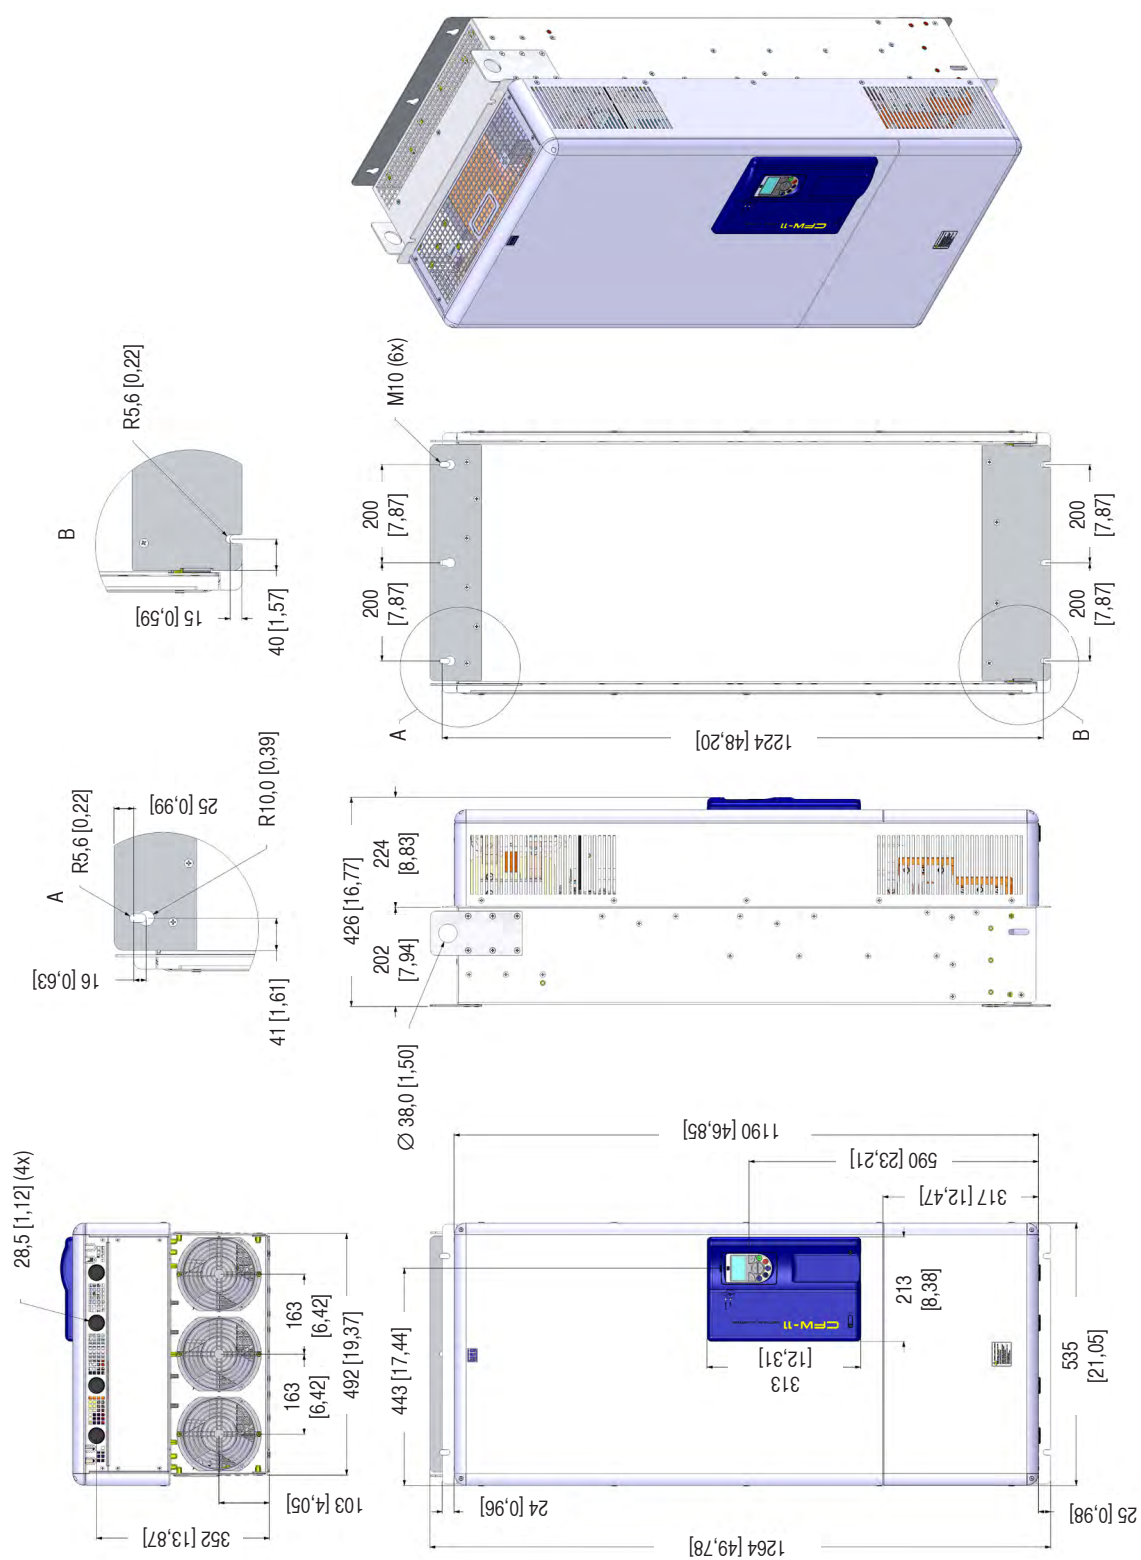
Размеры корпуса G, мм [дюйм.]
